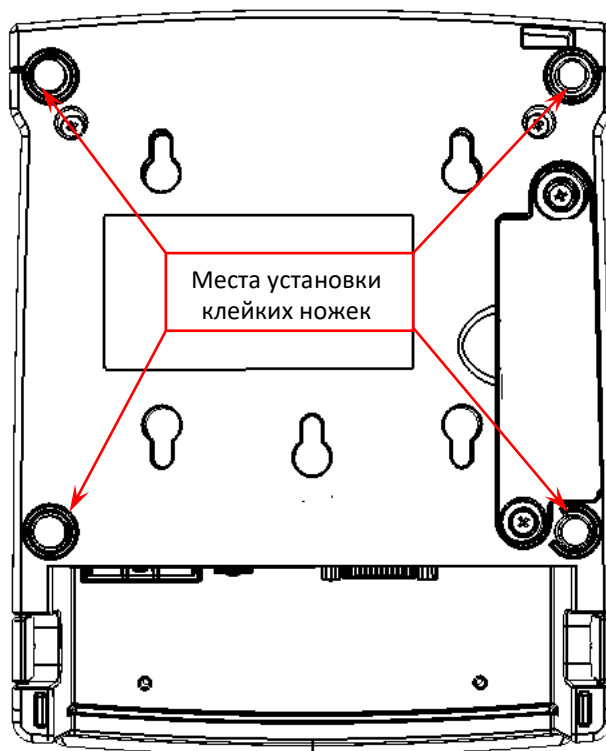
Места установка клейких ножек на дне корпуса изделия
